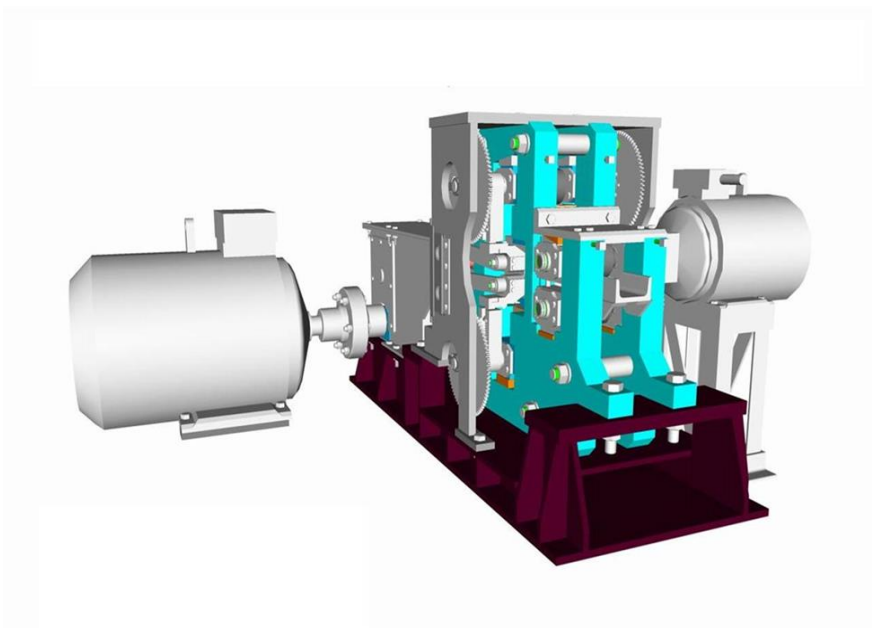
Общий вид лабораторного маятникового стана с цепным приводом
